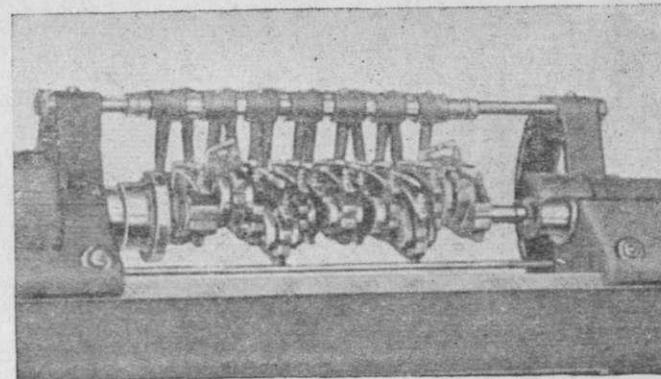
Коленчатый вал, установленный на станок фирмы Нортон, с надетыми на шейки шарнирными хомутами для лепинга.
